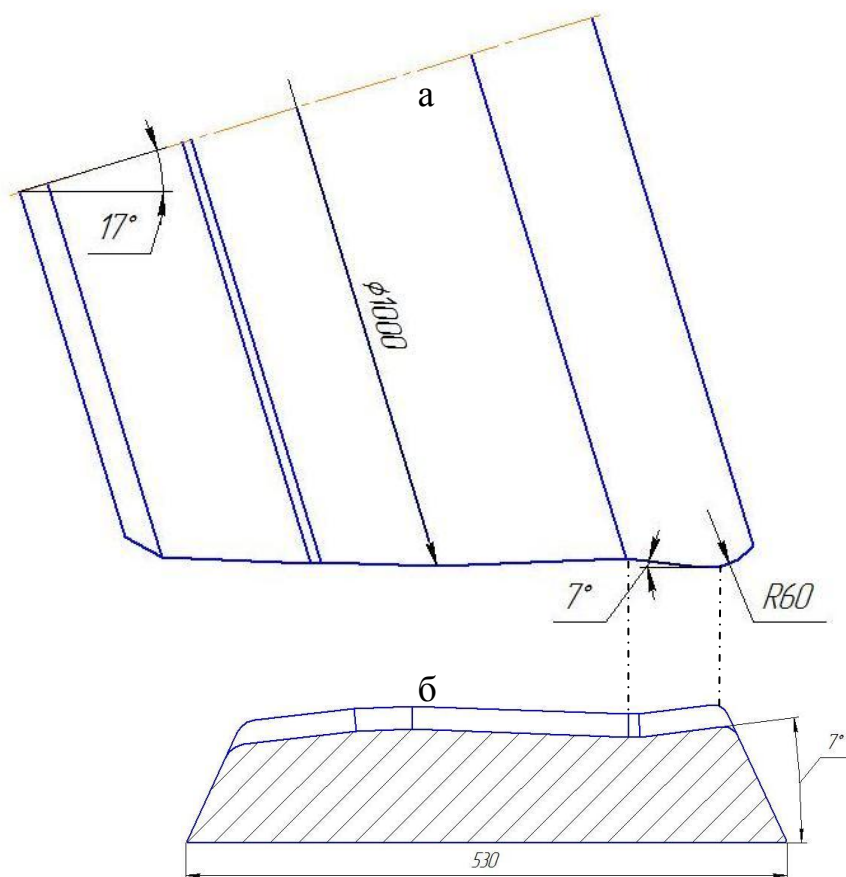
Калибровка технологического инструмента прошивного стана для прошивки заготовок повышенного диаметра (ОАО «СинТЗ»): а – валок; б – линейка
